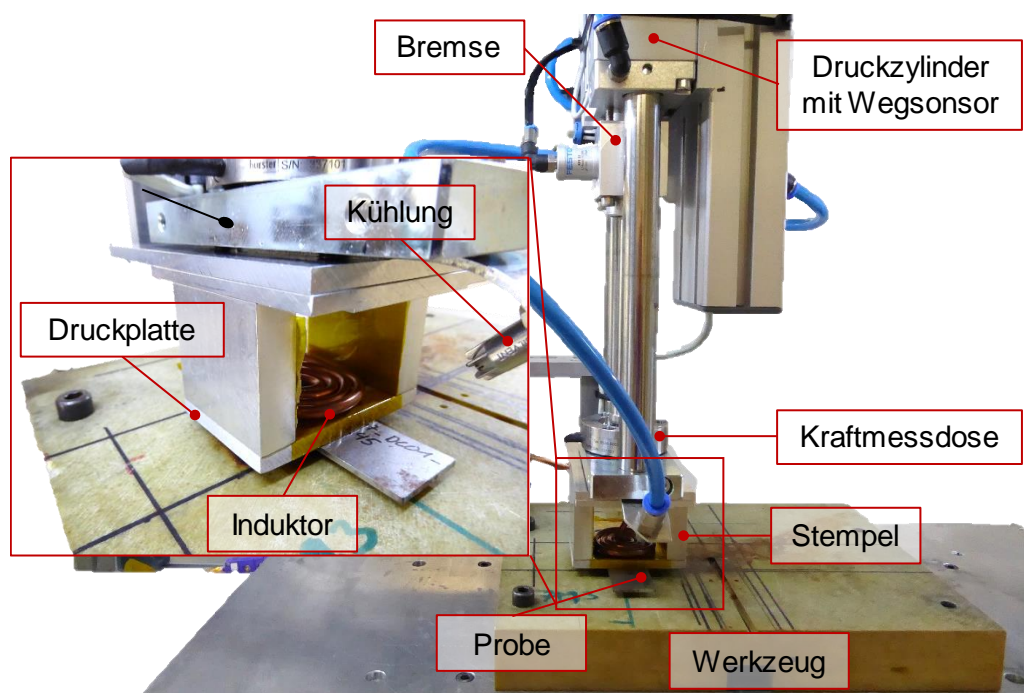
Versuchsaufbau zum weggeregelten Schweißen
